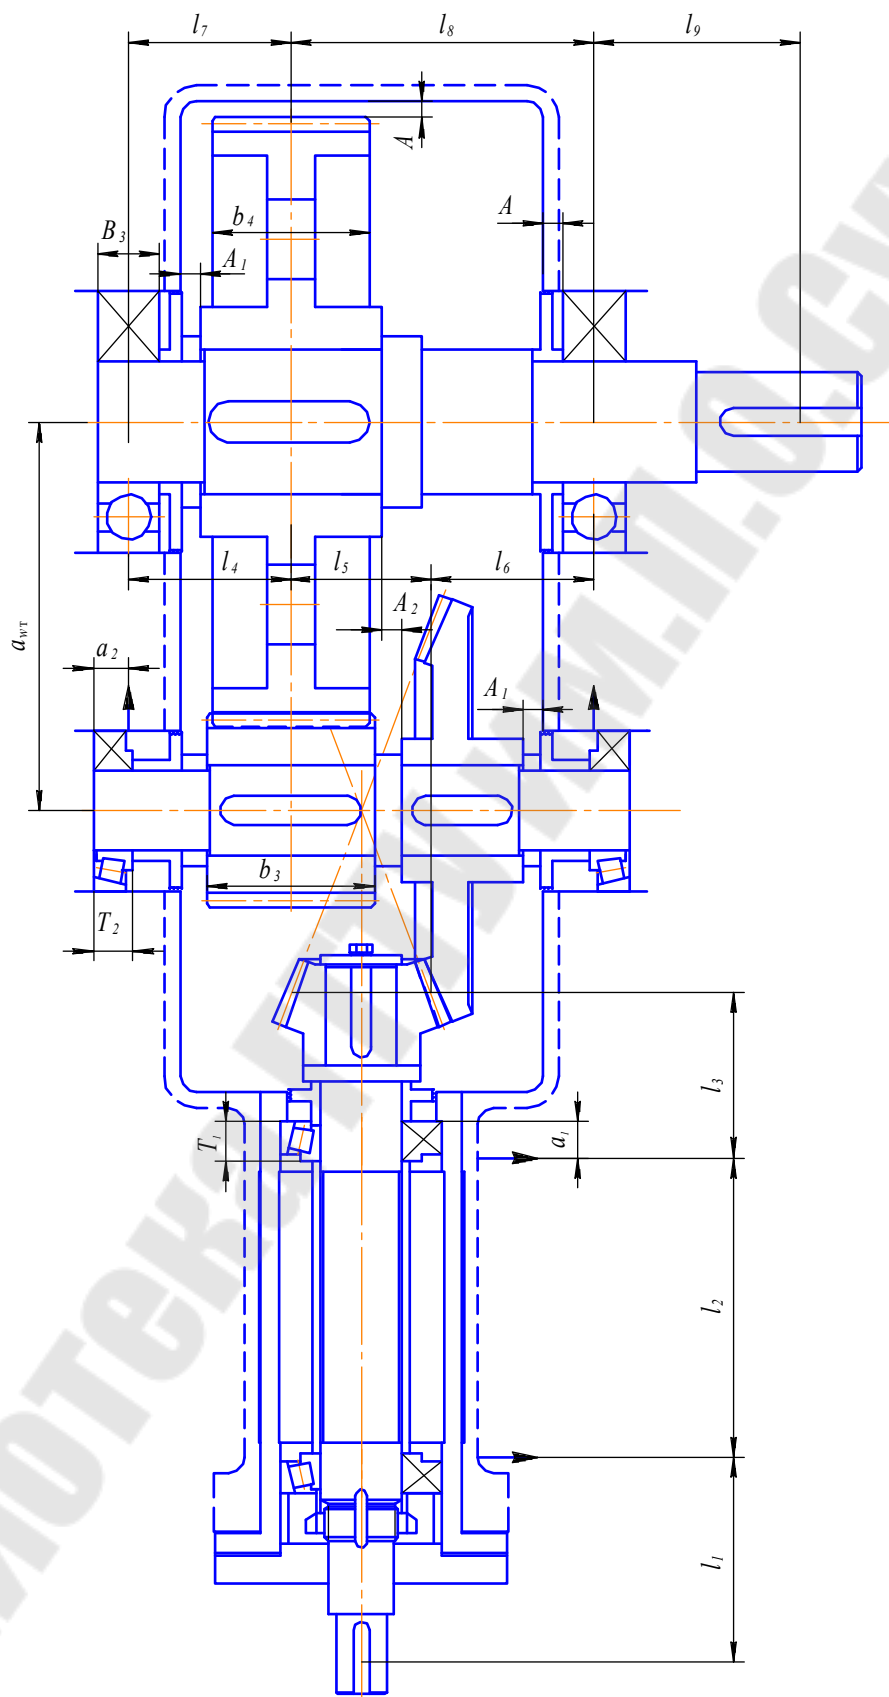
Компонувочная схема коническо-цилиндрического редуктора
